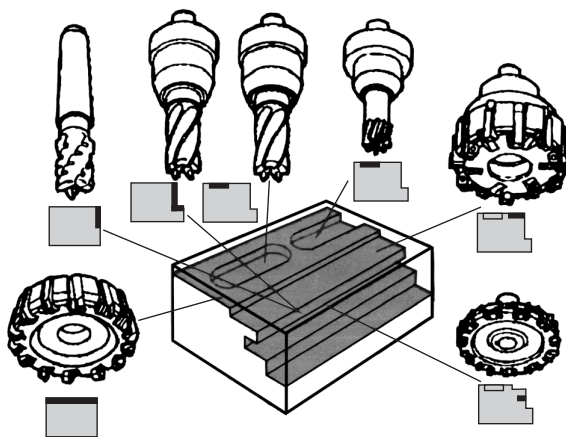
Схема зон и расположения инструментов при фрезерной обработке детали
